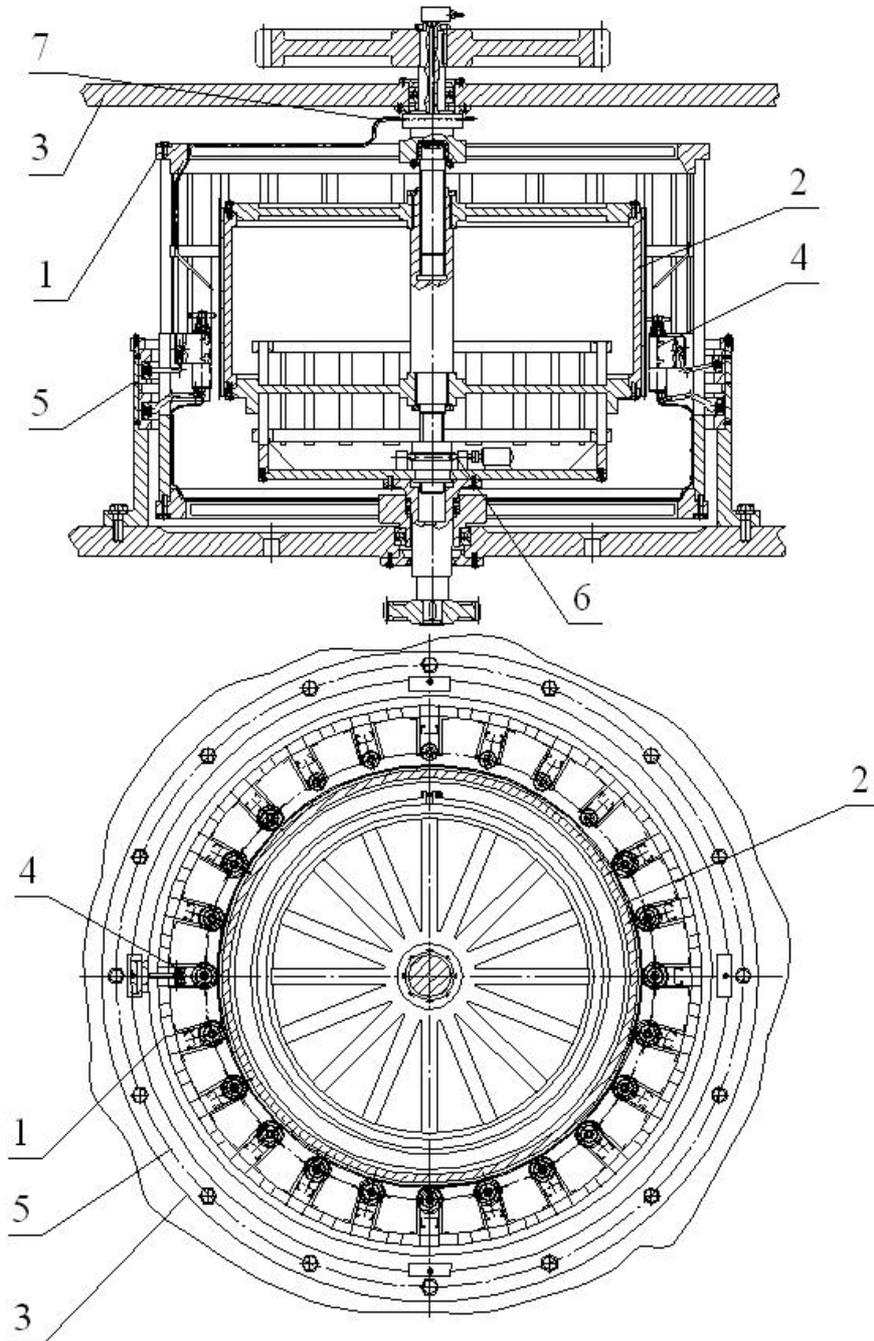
Конструкция роторного автомата для хонингования зубчатых колес:
